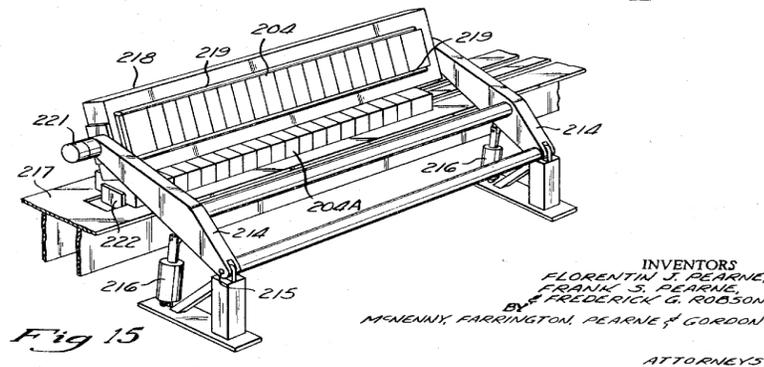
Patente 3 – Brick making machine. Patent Num: 3,589,495.
